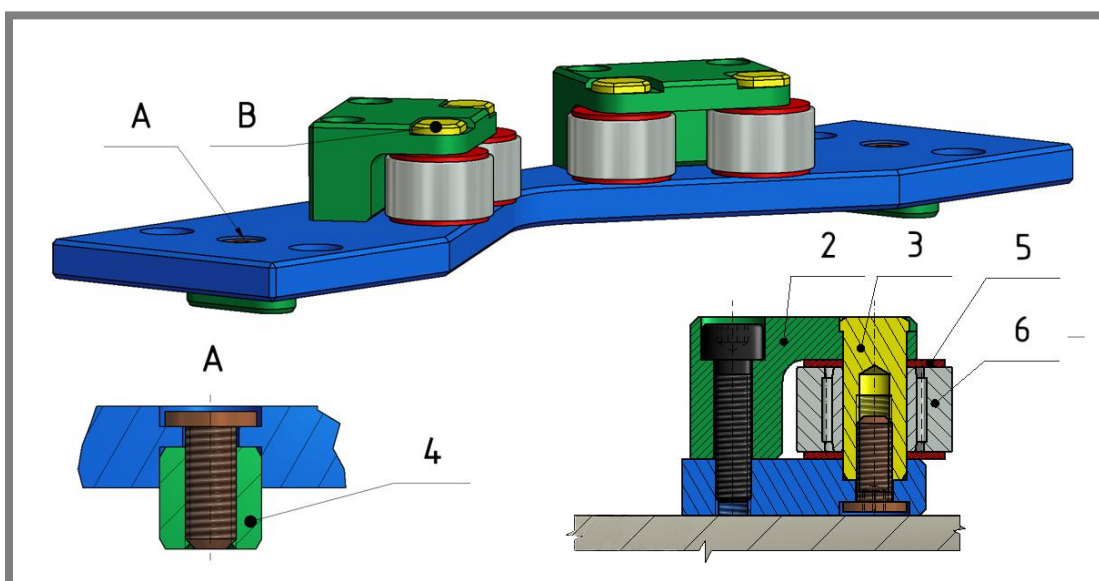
Varianta 4 – Deska s točnou a ložisky
